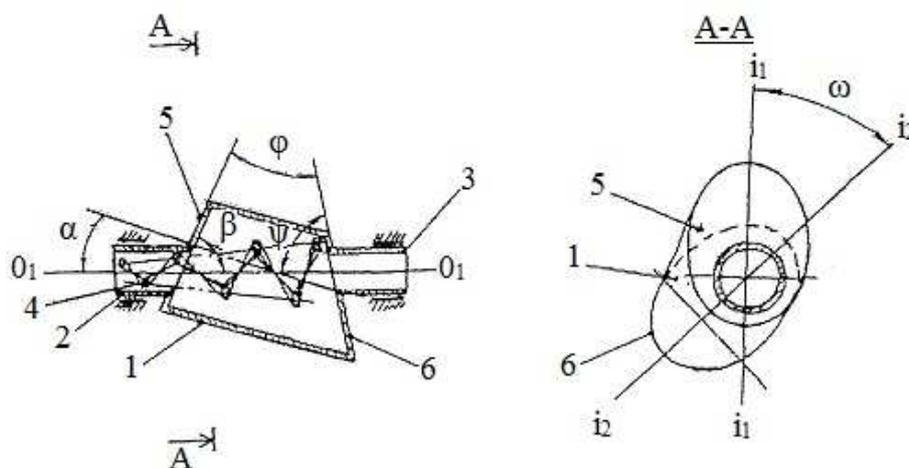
Установка барабанная для непрерывного приготовления кормов:
